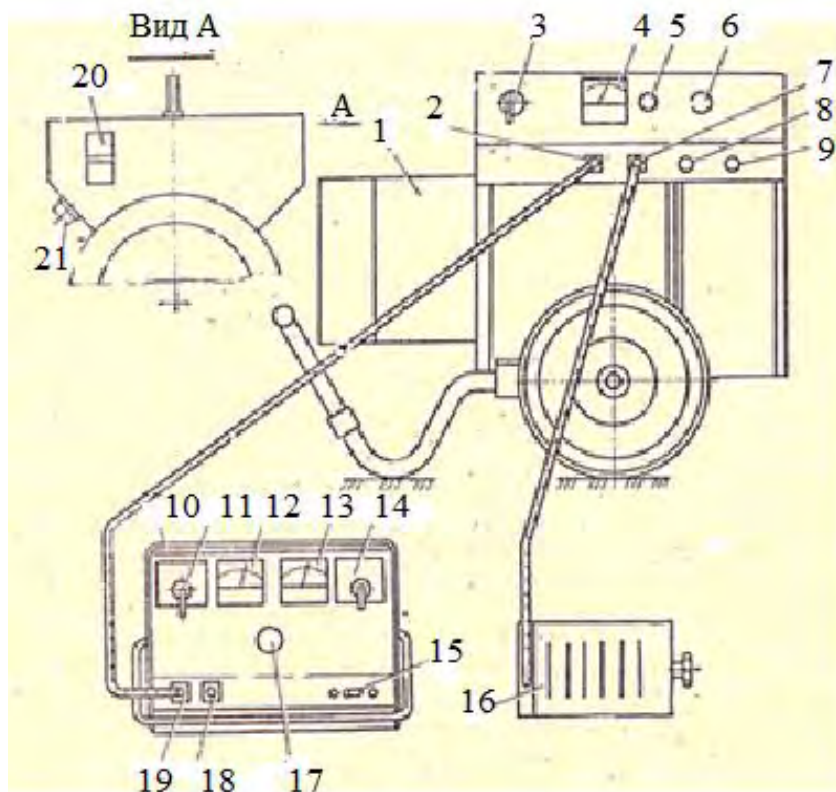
Сварочно-зарядная установка УДЗ-103У2:
